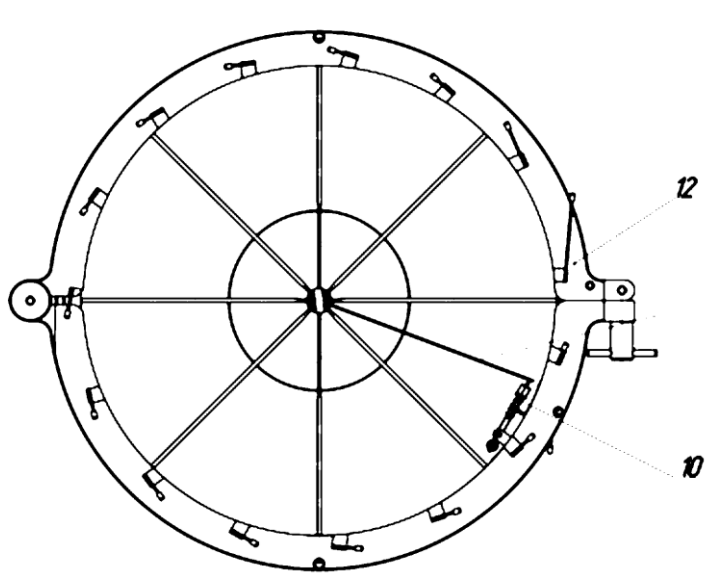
Конструкция замка для регулирования настройки приспособления
